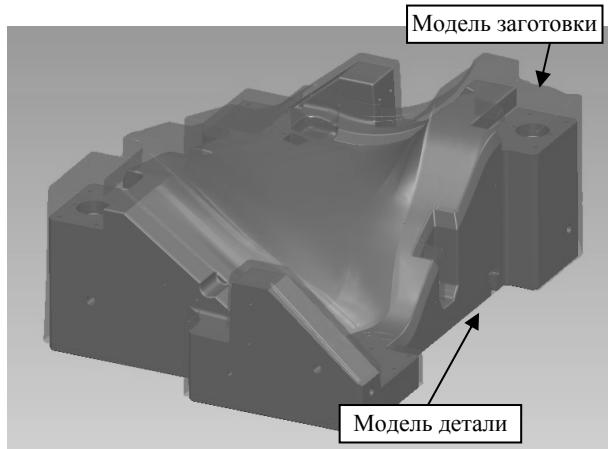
Ориентация модели детали относительно построенной модели заготовки
